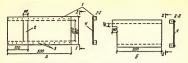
Конструкции шаблонов для разметки паза (а) и шипа (б): 1 — рейка; 2 — контур пропиле; 3 — гвозди; 4 — фанера
